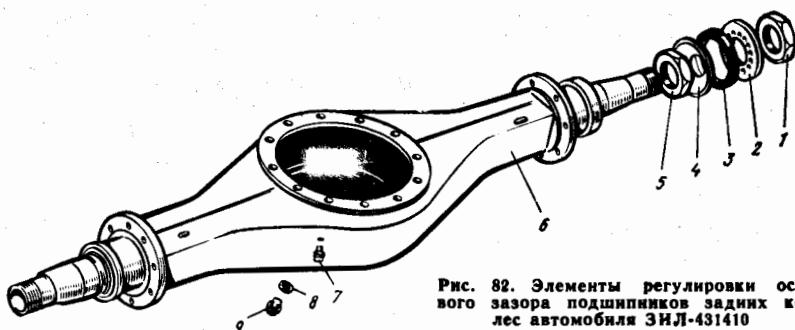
Элементы регулировки осевого зазора подшипников задних колес автомобиля ЗИЛ-431410
